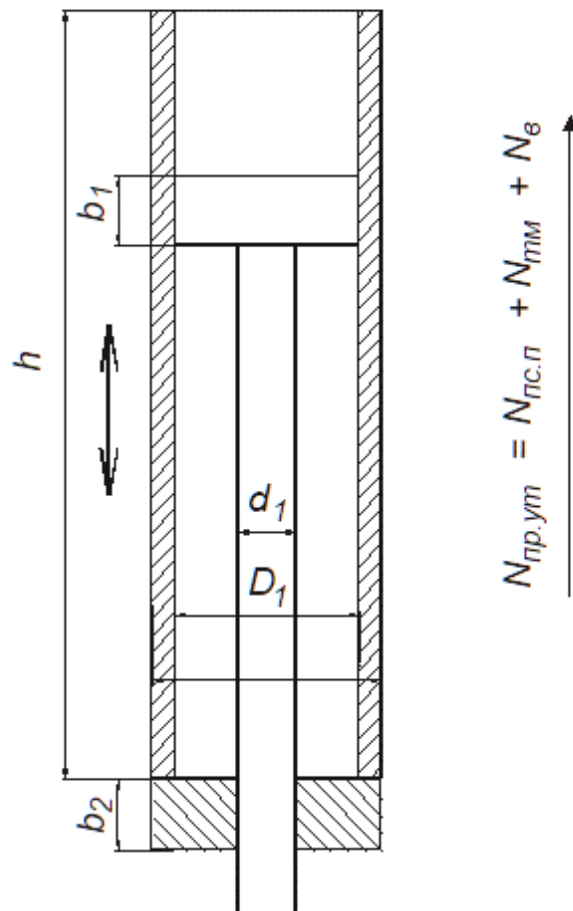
Розрахункова схема пневмоциліндра
